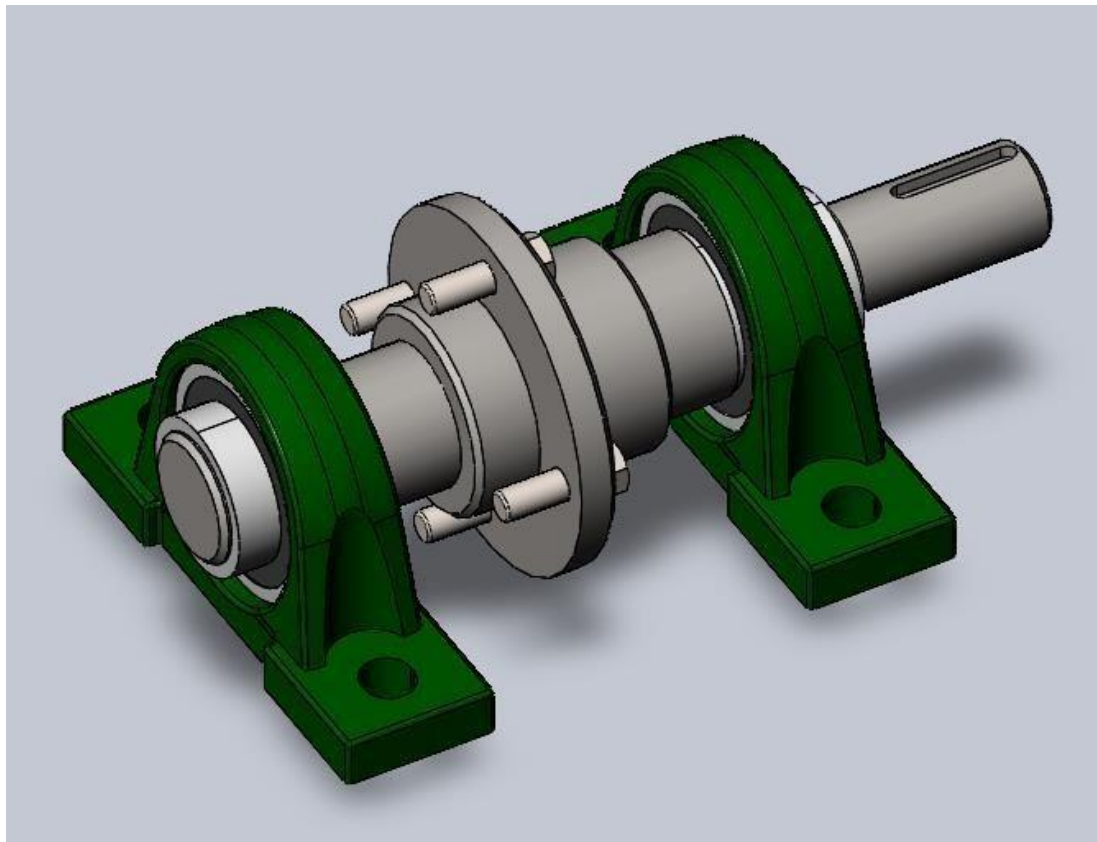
Конструкція вузла приводу подрібнювача
